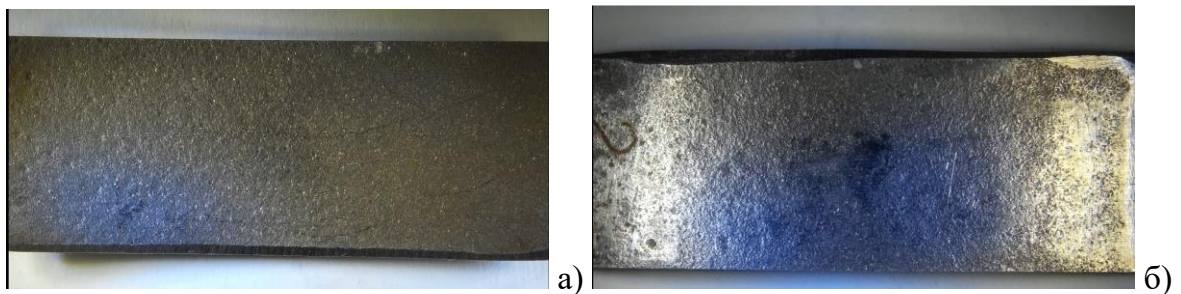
Съемный литой образец – имитатор пера лопатки из стали 08X14H7МЛ: а) вогнутая часть; б) выпуклая часть [2]
